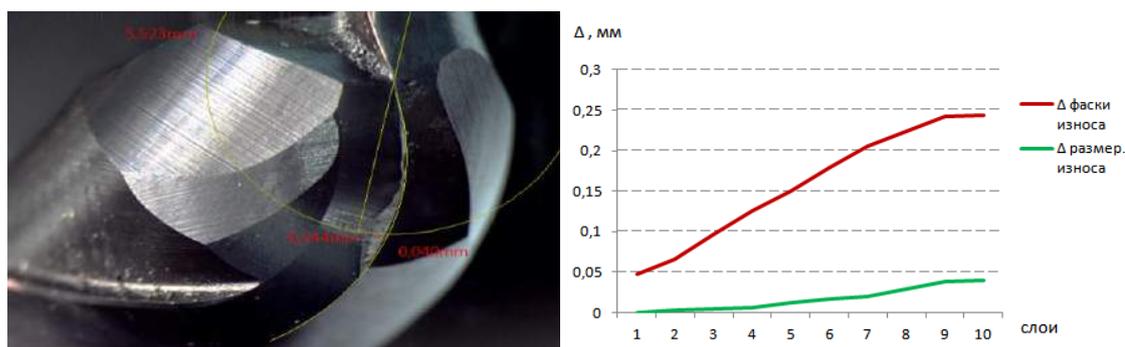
Фаски износа по задней поверхности сферических концевых фрез после обработки образца материала под углом 45°
